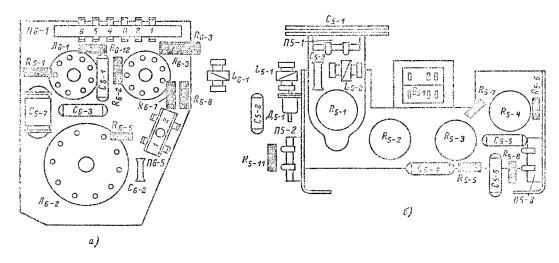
Вид со стороны монтажа на блоки строчной развертки (а) и блок регулировки (б) телевизора «Вечер».
